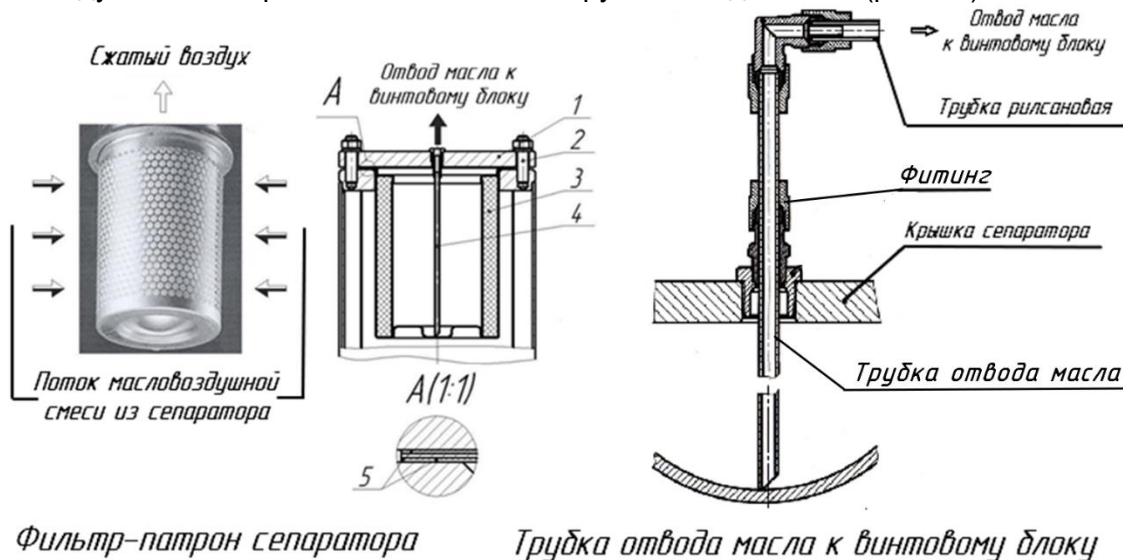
Схема фильтра-патрона сепаратора: 1 - крышка сепаратора; 2 - шпилька; 3 - фильтр-патрон; 4 - трубка отвода масла к винтовому блоку; 5 - прокладки.
